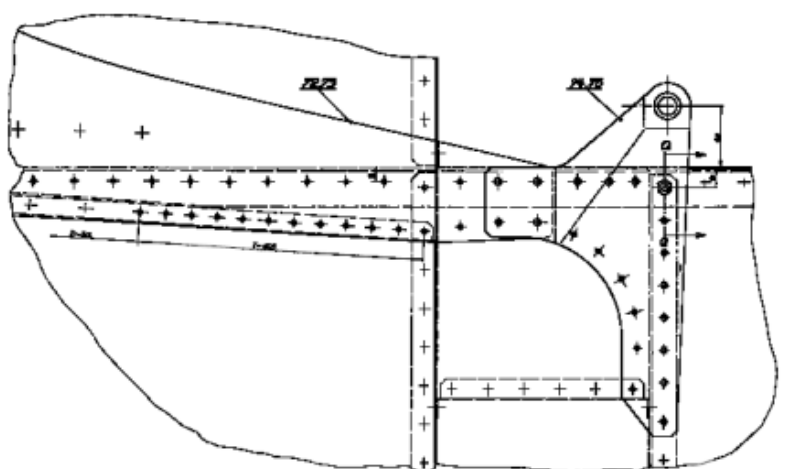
disegno della piastra rivettata alla struttura (fonte Pilatus).
